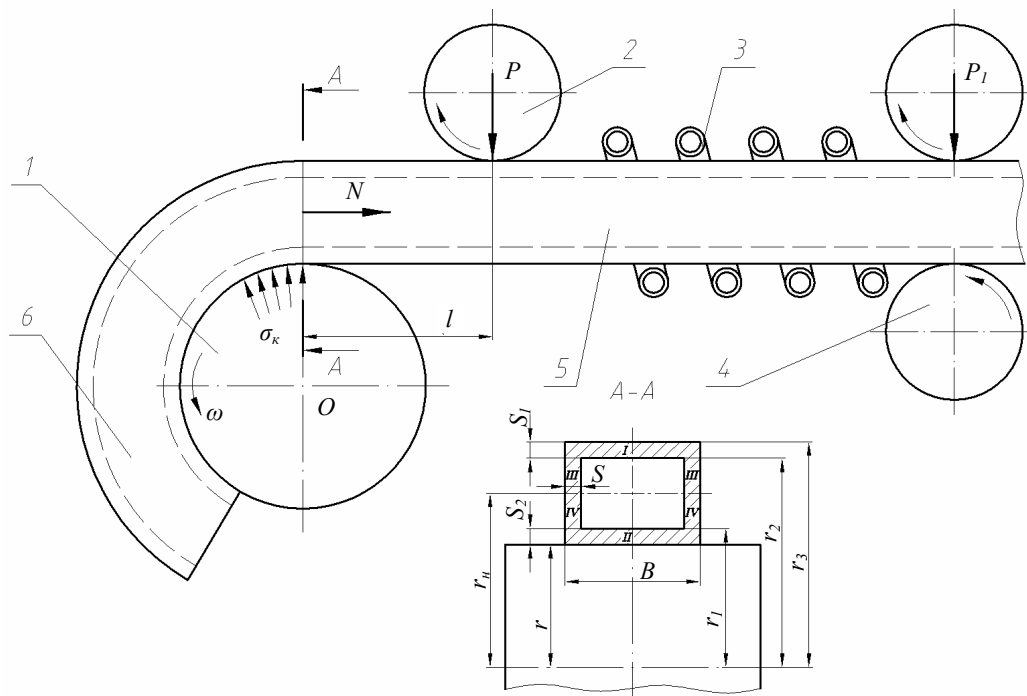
Розрахункова схема процесу формоутворення соленоїдів з труб прямокутного поперечного сечення:
